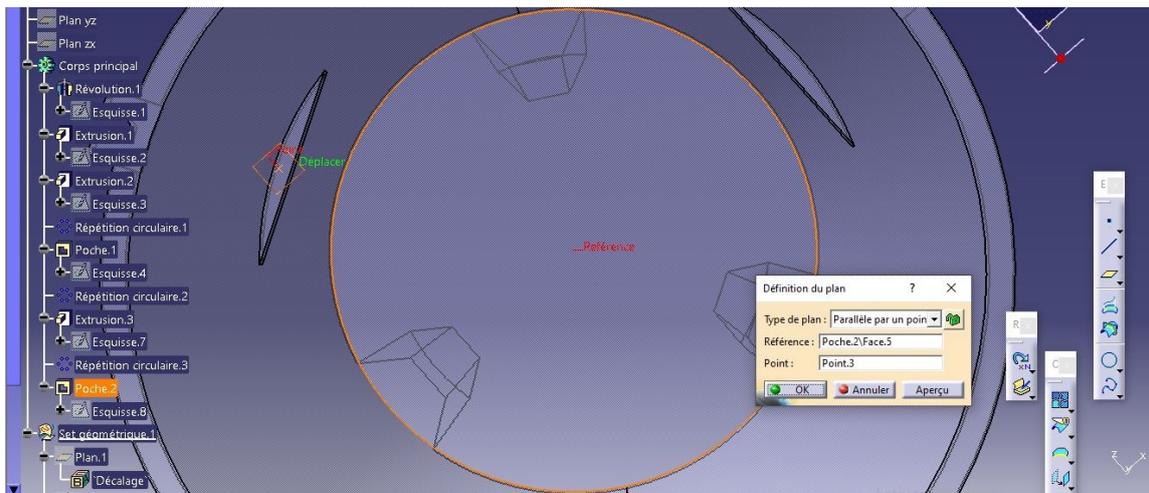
Définition des paramètres du plan sur « Surface design »
